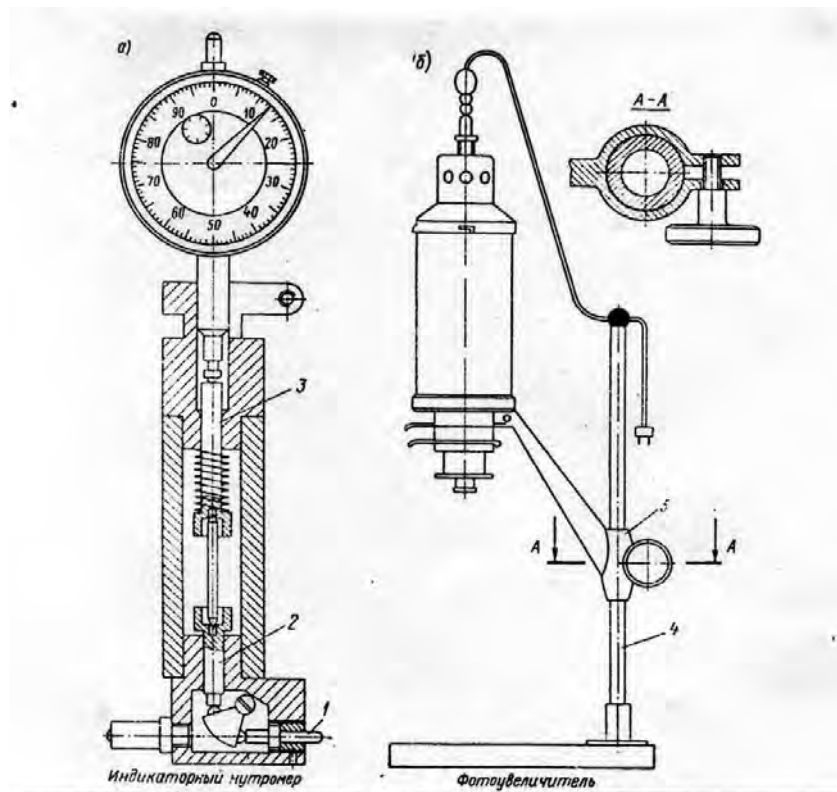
Индикаторный нутромер и фотоувеличитель
